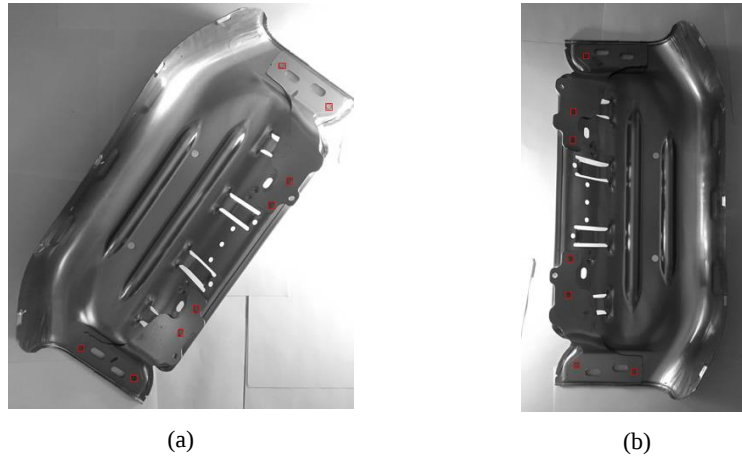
Autopartes fabricadas, manualmente etiquetadas. a) Con 8 puntos de soldadura (no defectuosa). b) Con 7 puntos de soldadura (defectuosa).
